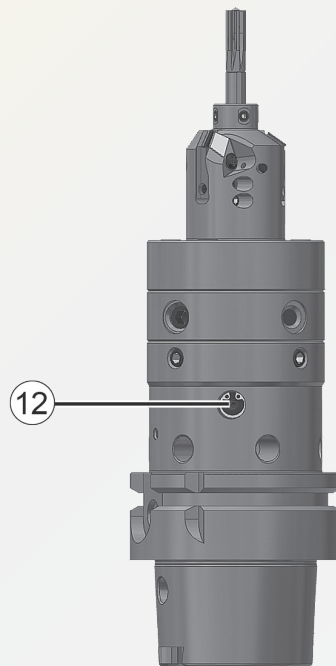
Sechskant-Spannschlüssel in Betätigungsschraube einstecken
